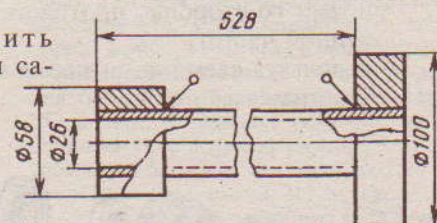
Подставка для запрессовки среднего подшипника с подушкой в сборе
